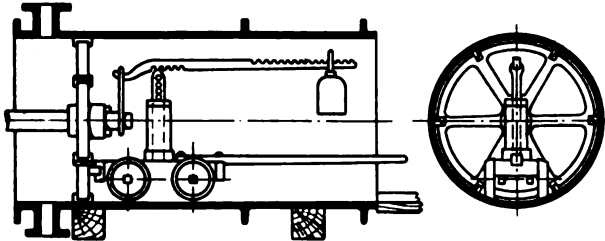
Ausgleich des Gewichtes der Bohrstange durch einen in der Bohrung laufenden Wagen mit Gegengewicht (*Smeaton* 1769)
